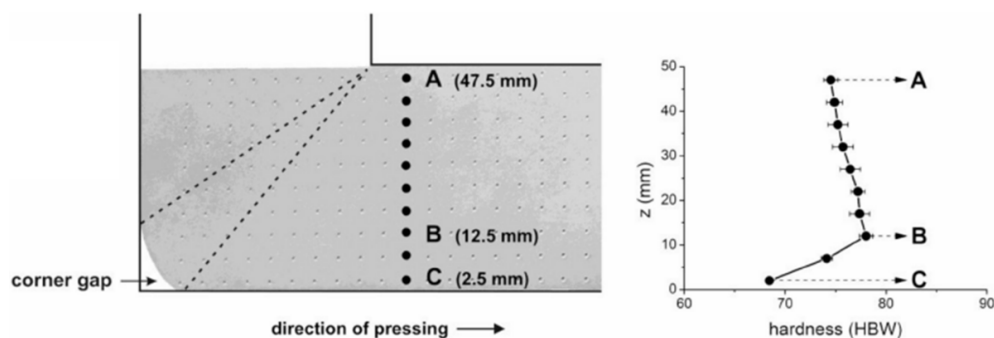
Härtemessung über den Querschnitt einer Aluminium 6060 ECAP-Probe mit ausgebildetem Corner Gap [Fri11]
